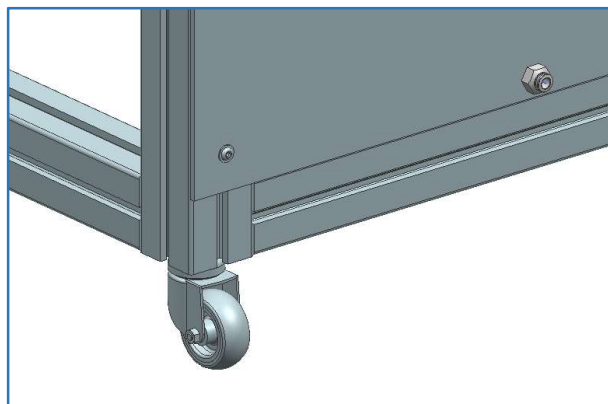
Vista particolare lato sinistro macchina: visibile vite bombata ed innesto pneumatico a parete
